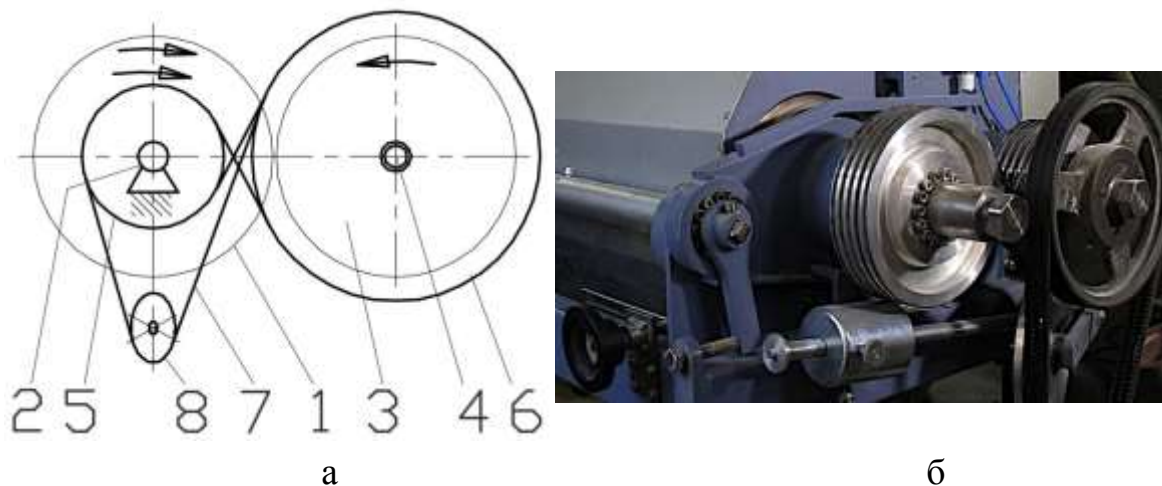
Міжвальцьова тросова передача (а) схема, (б) загальний вигляд.
